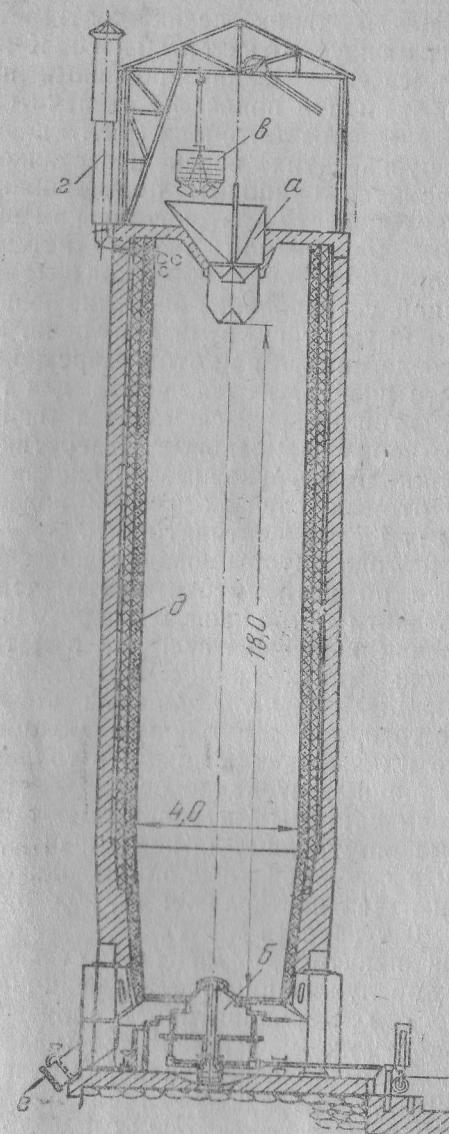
а—загрузочное устройство; б—автоматический выгрузной механизм; в—вагонетка воздушной канатной дороги; г—резервная труба для выпуска отходящих газов в атмосферу; д—футеровка шахты; е—выпуск извести из печи.
